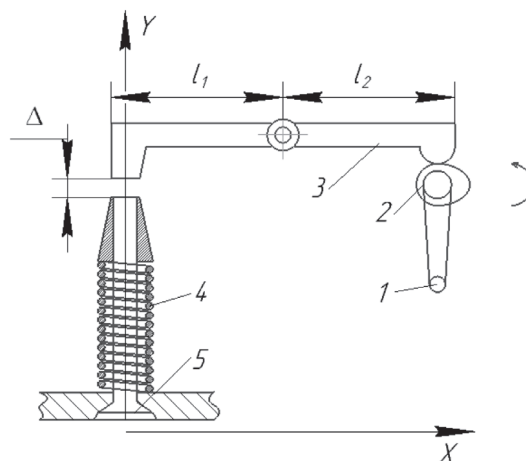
Структурная схема механизма газораспределения одиночного клапана: 1 – ведущая звездочка коленчатого вала; 2 – кулачок; 3 – коромысло; 4 – пружина; 5 – клапан; Δ – тепловой зазор.
